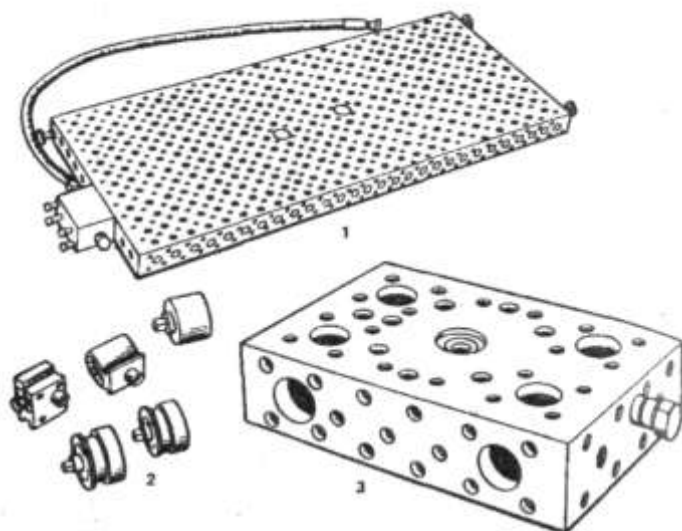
Базовые плиты и гидроцилиндры: 1 — плита базовая, 2 — гидроцилиндры, 3 — блок гидравлический
